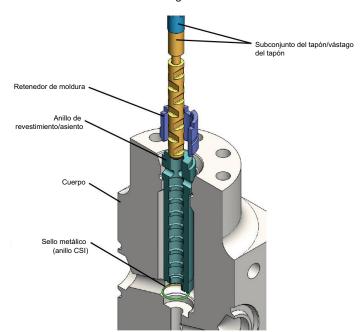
Vista despiezada del conjunto de regulador -Revestimiento Integral/Anillo de Asiento (desequilibrado 1")
